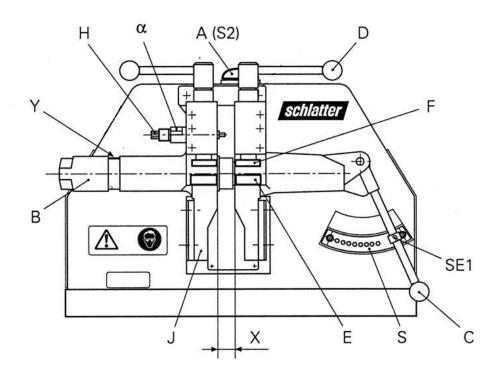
Máquina de soldar a topo tipo M, tabela de ajuste
